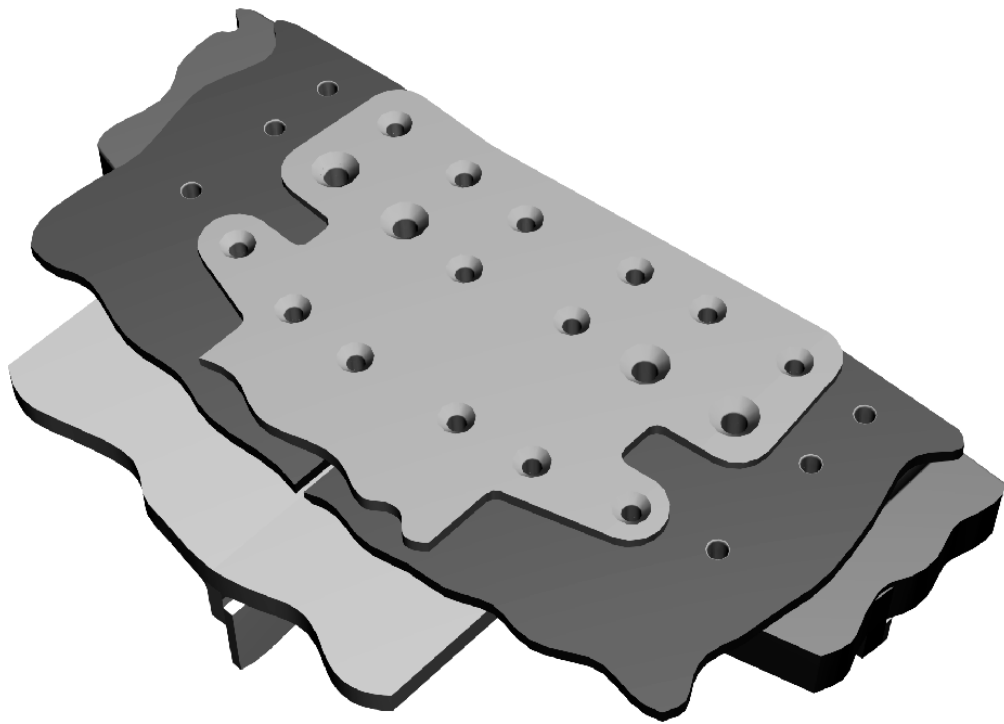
Заготовка вузла з отворами під кріпильні елементи
